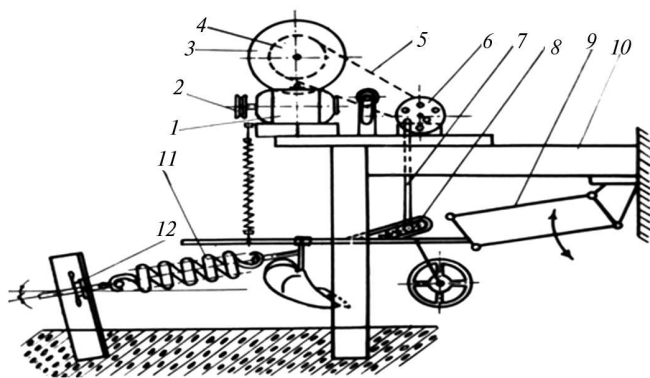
Схема стенда для испытания деталей шарниров грядил культиватора КРХ-4:
